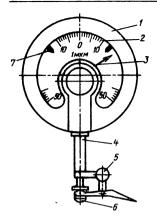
Микатор: I — корпус; 2 — шкала; 3 — стрелка; 4 — гильза; 5 — арретир; 6 — измерительный наконечник; 7 — указатели поля допуска
